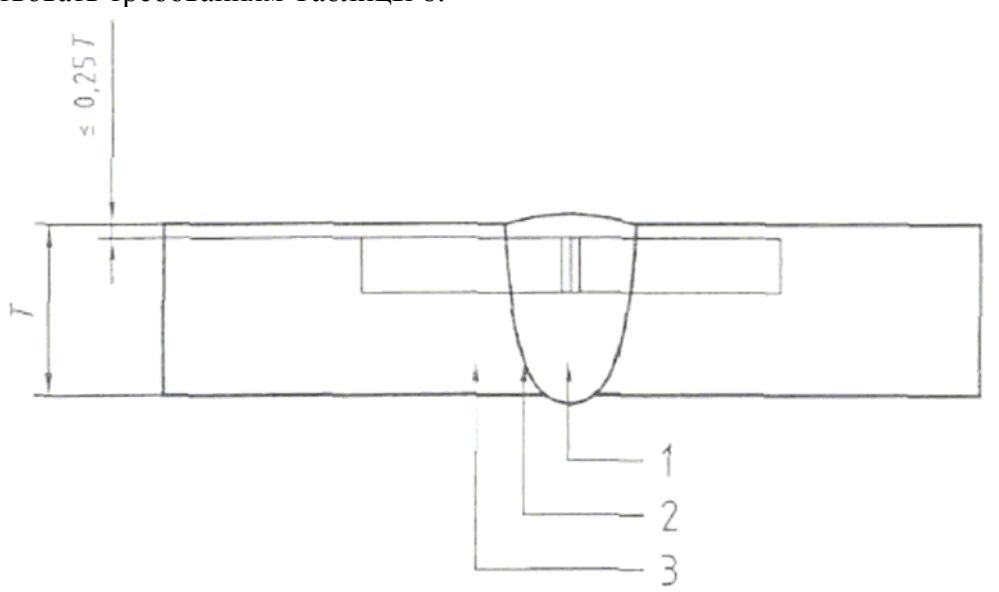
Местоположение образца металла сварного с V-образным надрезом по Шарпи.
